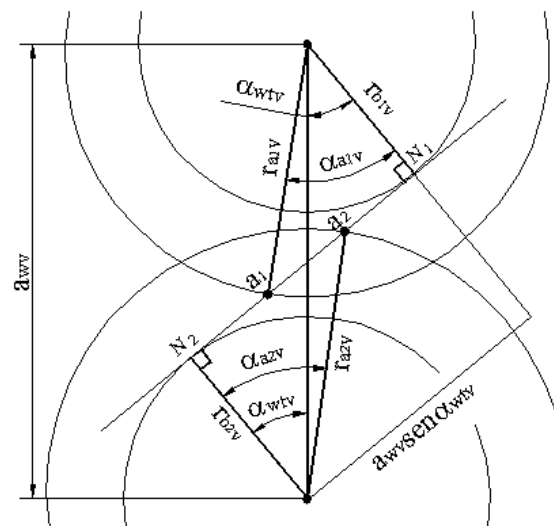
Engranaje cilíndrico virtual (Vista axial).
